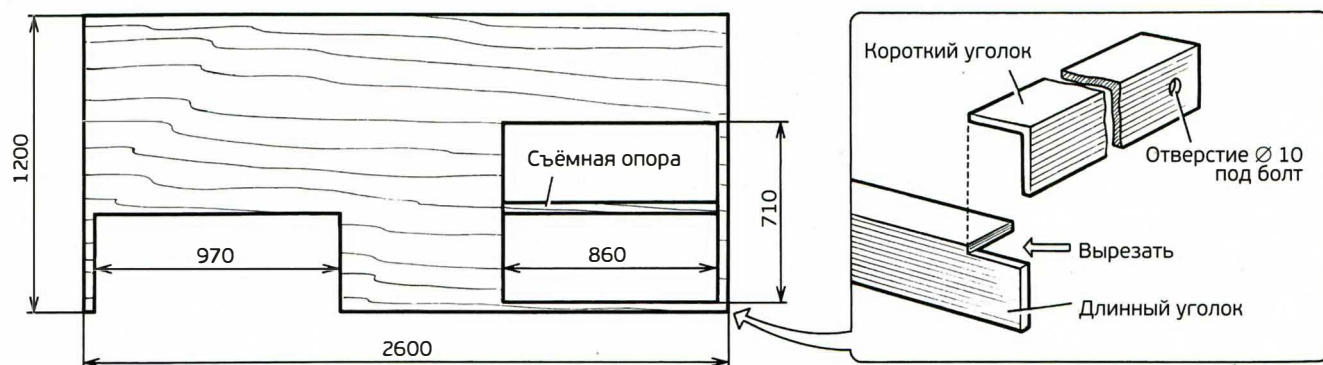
План столешницы и подготовка уголков для соединения сваркой.
